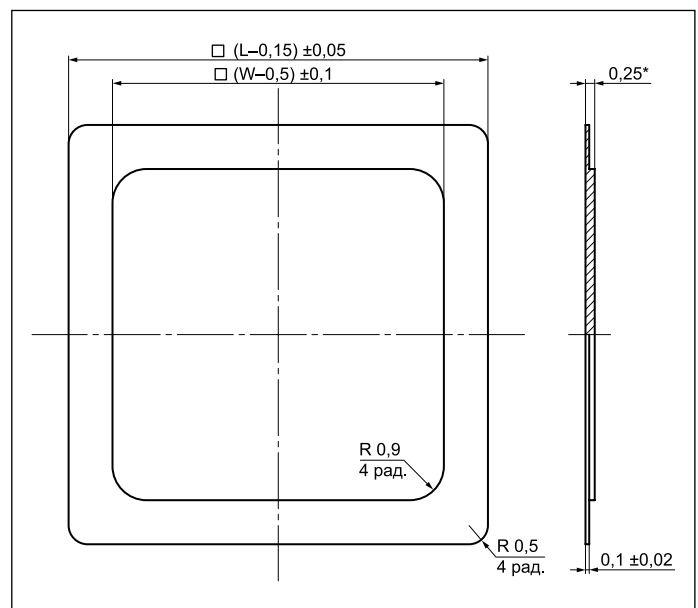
Чертеж ступенчатой крышки металлокерамического корпуса
